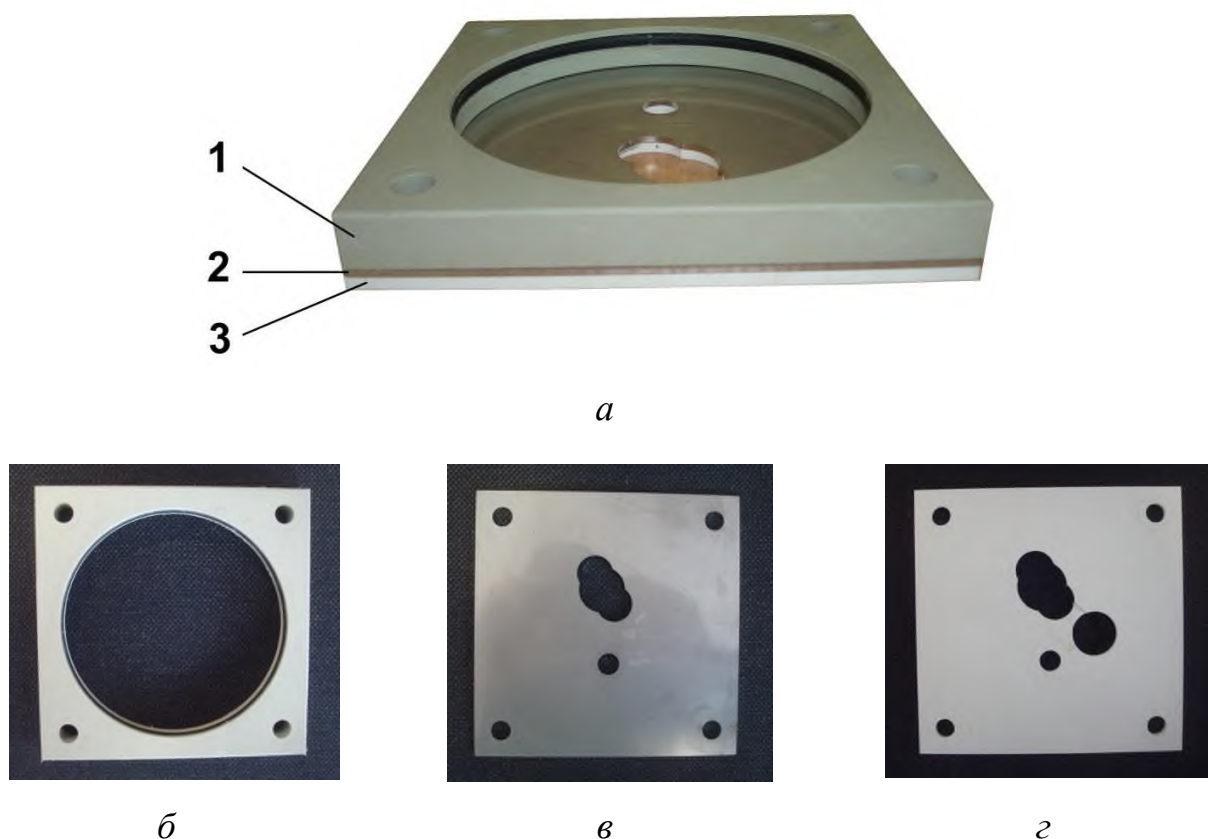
Накладка: а – загальний вигляд; б – верхня пластина; в – середня пластина; г – нижня пластина; 1 – верхня пластина; 2 – середня пластина; 3 – нижня пластина
